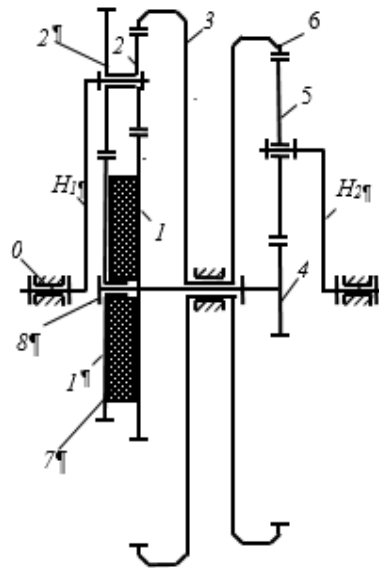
Уравновешенный двух подвижный зубчатый механизм с замкнутым контуром
